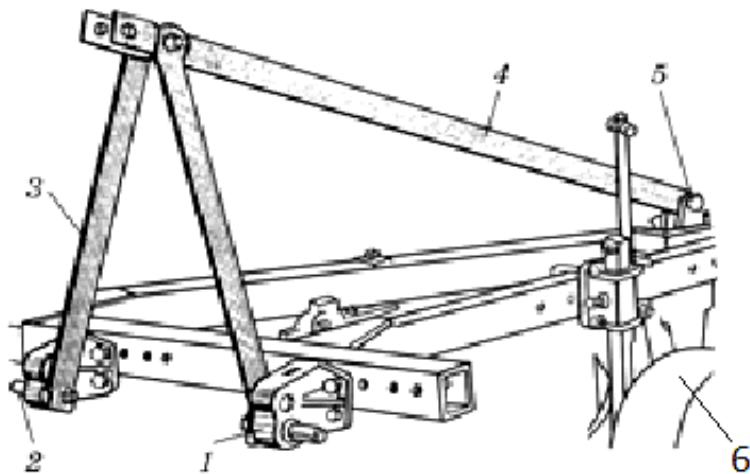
Начіпний пристрій з опорним колесом плуга ПЛН-5-35:
